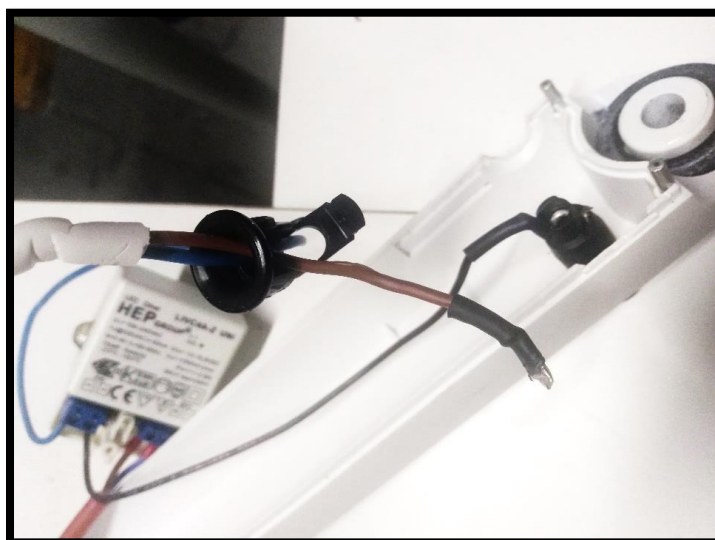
Cabo da fase, a castanho, dessoldado do fusível de proteção.
